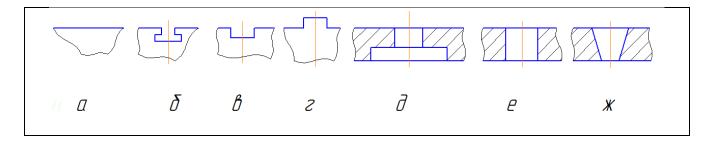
Унифицированные конструктивные элементы: а — плоскость; б —Т-образный паз; в — П-образный паз; г — П-образный выступ; д — цилиндрически выточка, е — цилиндрическое отверстие; ж — коническое отверстие
